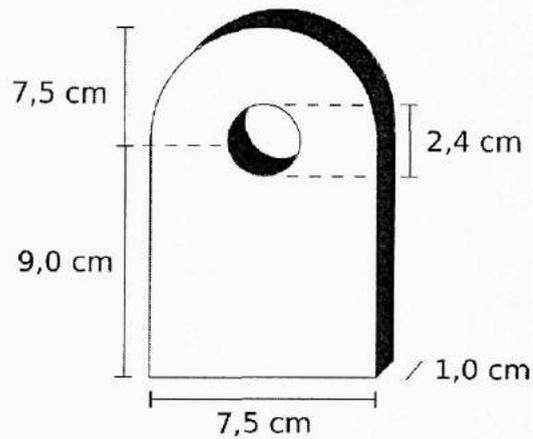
Desenho técnico do suporte do canhão de luz.
